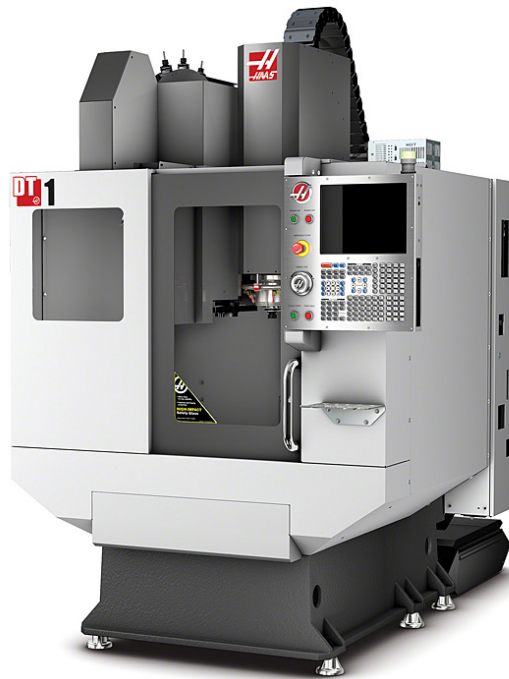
Вертикальний свердлильний верстат з ЧПУК HAAS DT-1
